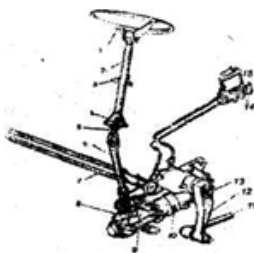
Рулевое управление автомобиля КамАЗ-4310: 1 - рулевое колесо; 2 - рулевая колонка; 3 - хомут; 4 - фланец; 5 - регулировочная гайка; 6-карданная передача; 7-радиатор; 8-распределитель; 9-угловой редуктор; 10-рулевой механизм; 11-продольная рулевая тяга; 12-сошка; 13-вал сошки; 14-насос; 15-бачок.
